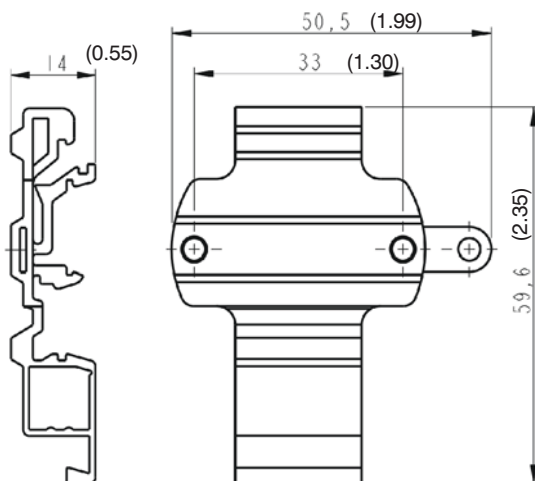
Dimensiones del perfil DIN simétrico (7NG3092-8KA)
